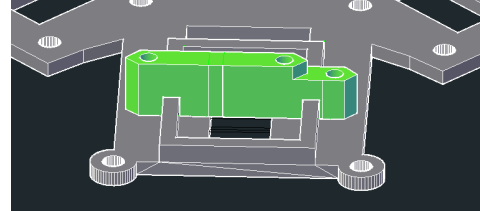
Adaptador impreso para sujetar el módulo Bluetooth.
